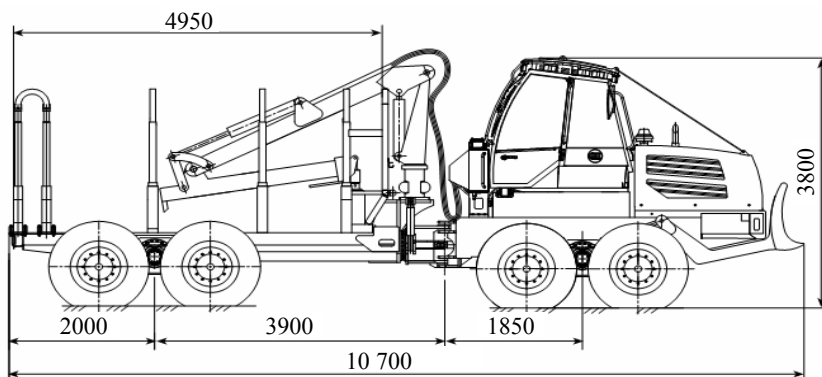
Общий вид форвардера «Амкодор 2682-01»
